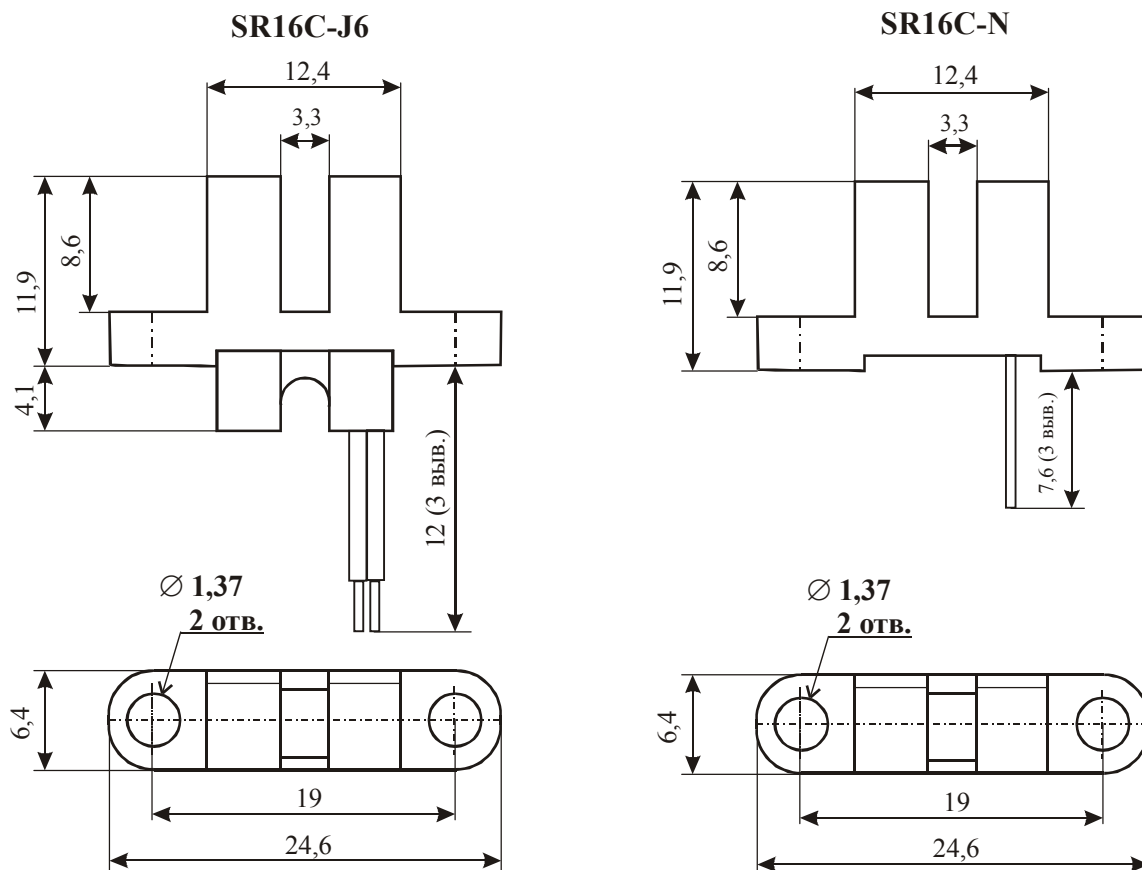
Внешний вид и габаритные размеры ЩМД типа SR16C-J6 и SR16C-N
